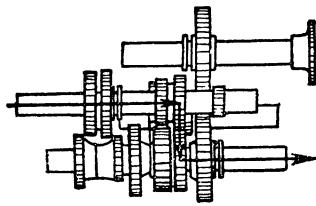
Схема расположения шестерен коробки. 5-я передача.
